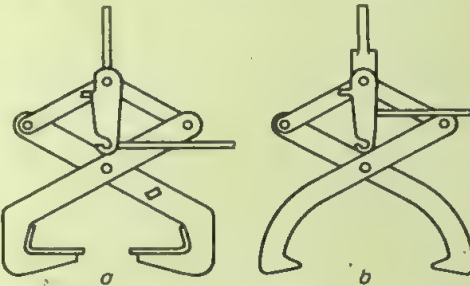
a Profilstahlzange, b Holzstammzange
